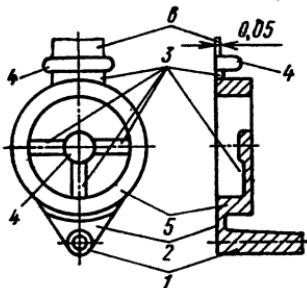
Промывники для цилиндрической отливки с внешней литниковой системой:
